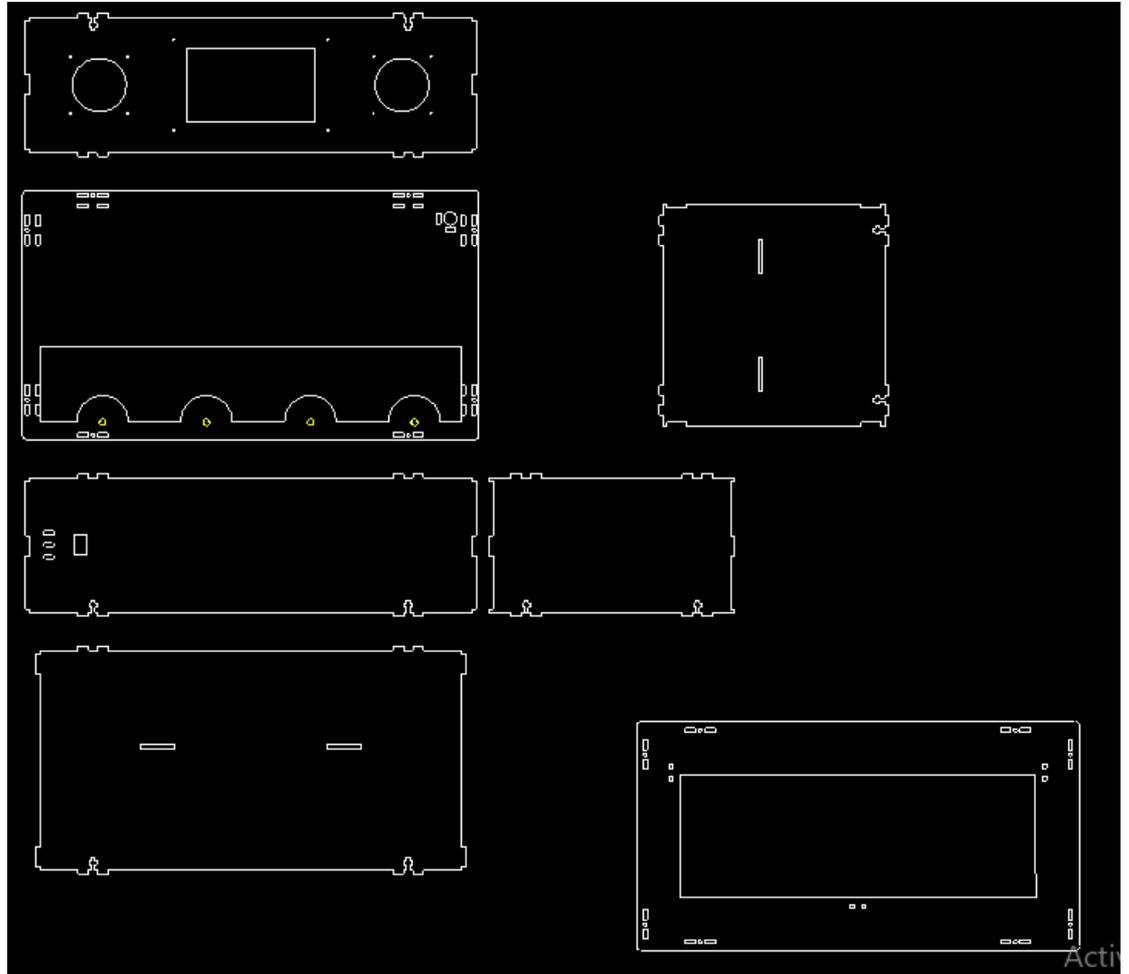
Diseño de corte del revestimiento para el prototipo dispensador de pastillas. Elaboración propia.
